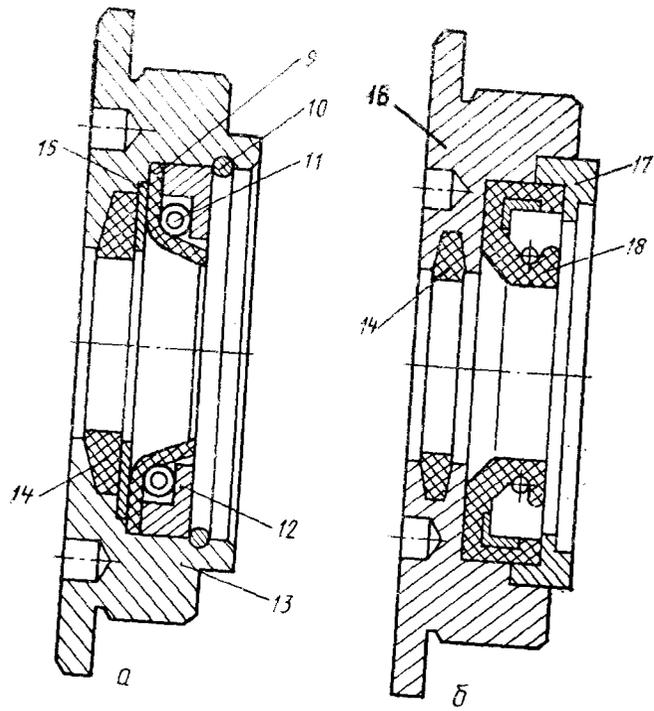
Установка червячного вала редуктора ветряка аэропыла:
